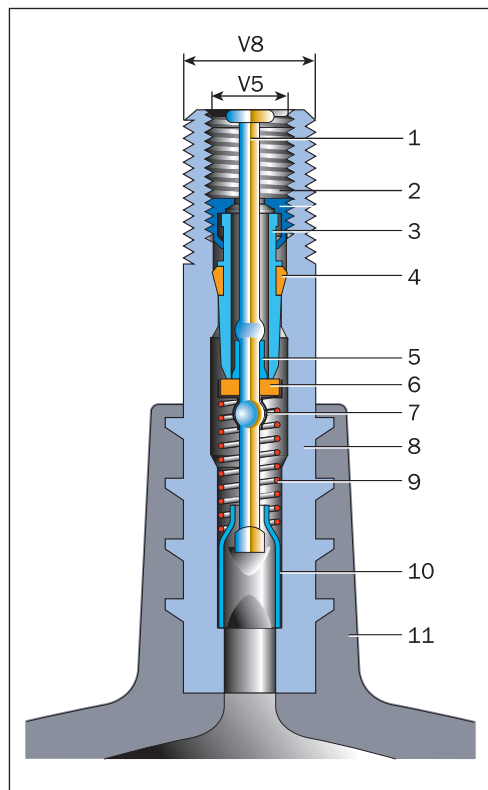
Вентиль камеры: 1 — стержень золотника; 2 — резьбовая головка; 3 — втулка; 4 — уплотнитель; 5 — верхняя чашечка; 6 — уплотнительное кольцо золотника; 7 — нижняя чашечка; 8 — корпус вентилья; 9 — пружина золотника; 10 — направляющая чашечка; 11 — обрезиненный кожух
